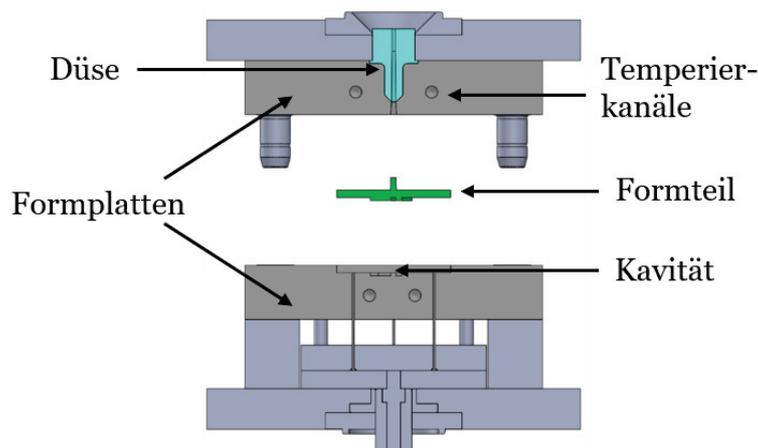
Grundlegender Aufbau eines Spritzgießwerkzeuges im geöffneten Zustand.
